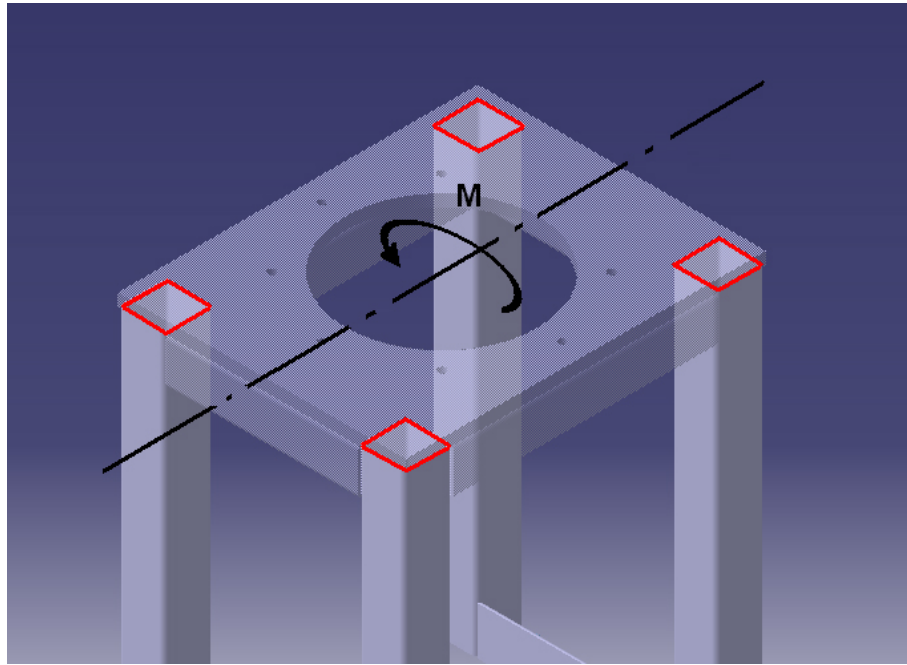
Aplicación del momento flector y posición de los cordones de soldadura
